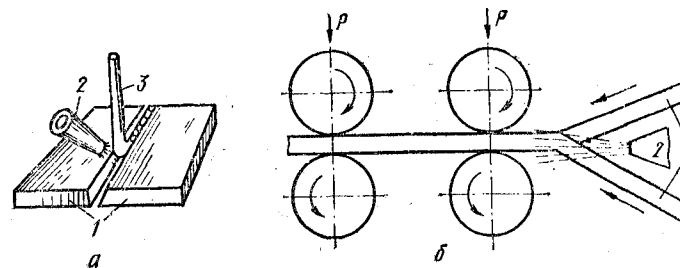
Схема сварки листов из термопласта горячим газом с присадочным (а) и без присадочного (б) материала
